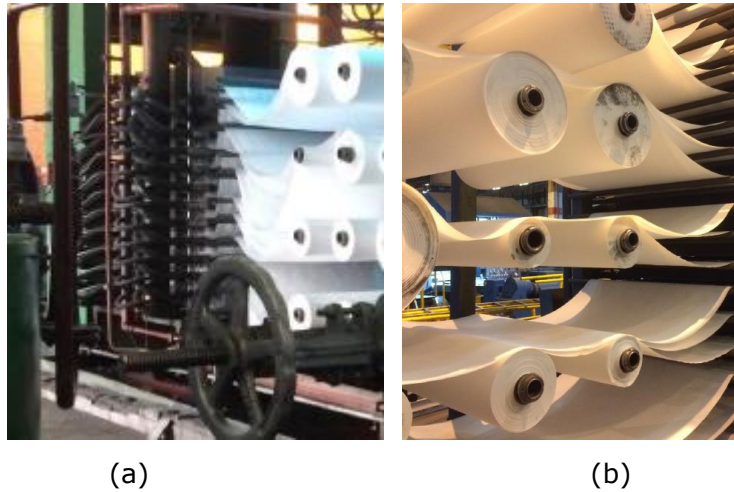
(a) Filtragem de um laminador a quente (b) Filtragem de um laminador a frio
